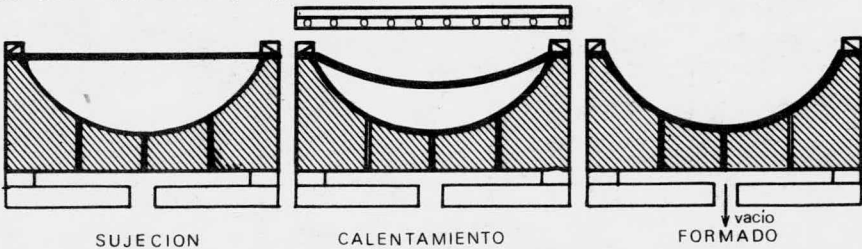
TERMOFORMADO DIRECTO CON VACÍO EN UN MOLDE HEMBRA
